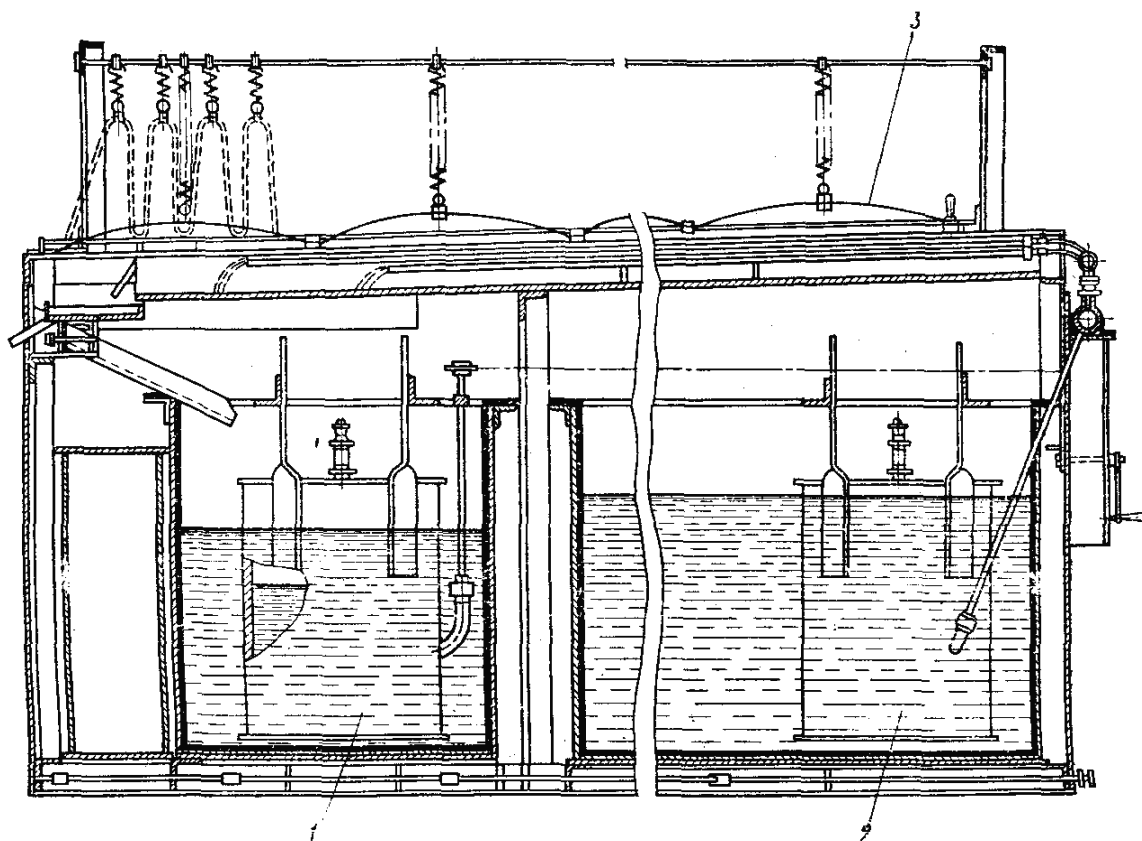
Установка для комбинированной очистки внутренних поверхностей металлических трубок:
